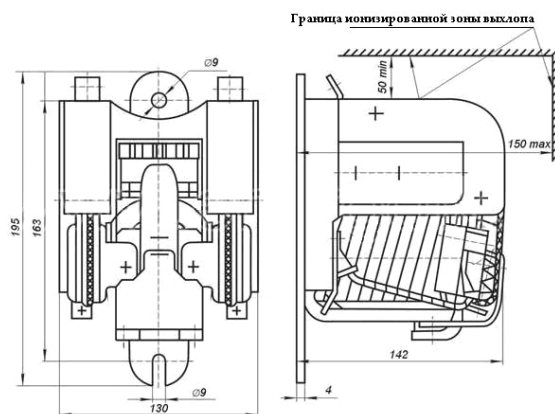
Габаритные, установочные размеры КПД-121 У2
